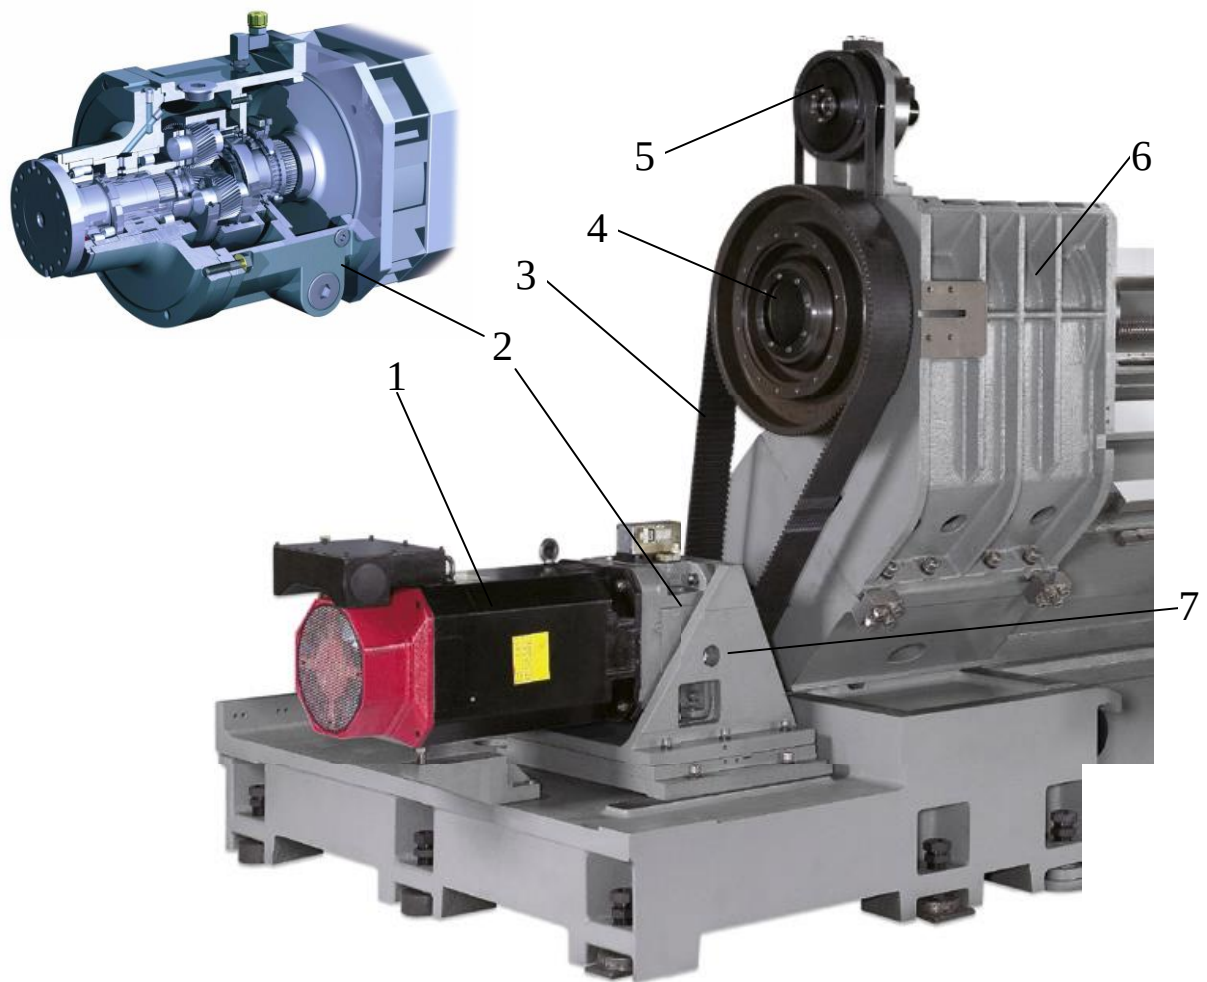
Привід головного руху з планетарною коробкою швидкостей: 1 – привідний двигун; 2 – планетарна коробка швидкостей; 3 – пасова передача; 4 – шпиндель; 5 – вимірювальна система; 6 – шпиндельна бабка; 7 – плита кріплення привідного двигуна з планетарною коробкою швидкостей.
